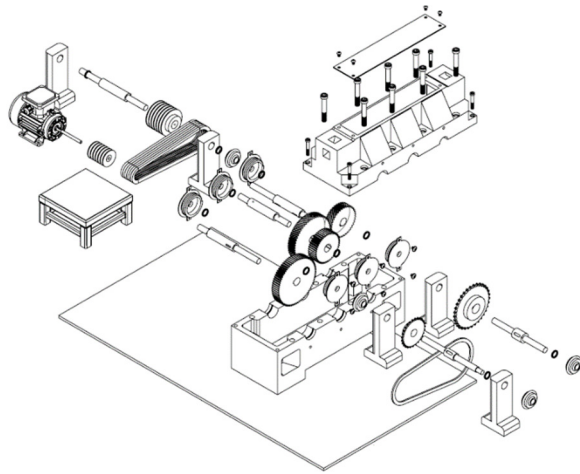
Plano de despiece o explosión del accionamiento mecánico
